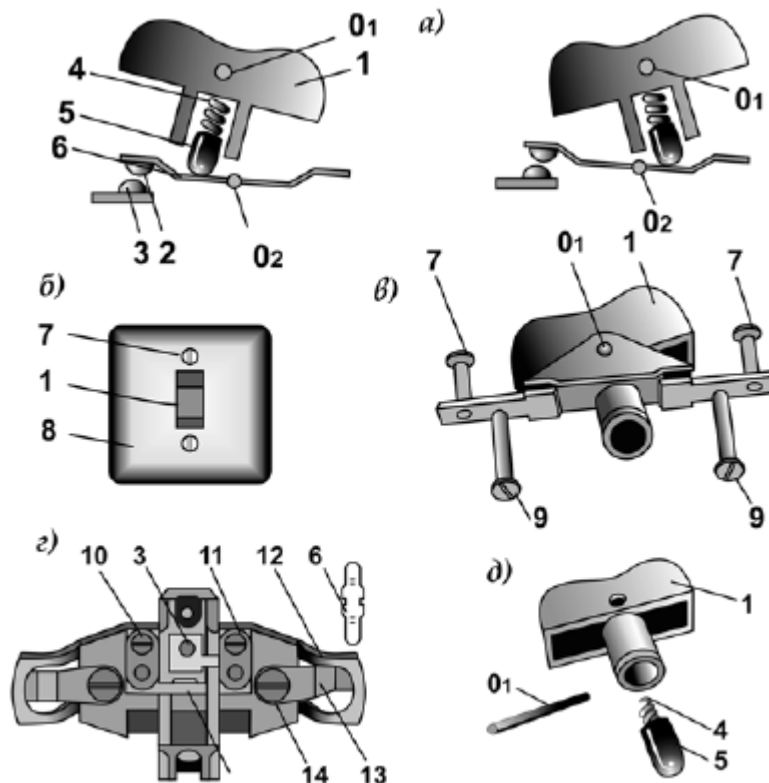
Выключатель с клавишным приводом для скрытой установки:
